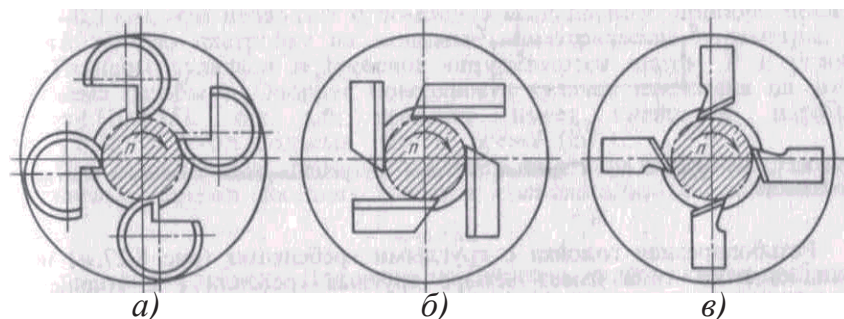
Нарезания резьб с использованием резьбонарезных головок: *а* – с круглыми гребенками; *б* – с плоскими тангенциальными плашками; *в* – с плоскими радиальными плашками
